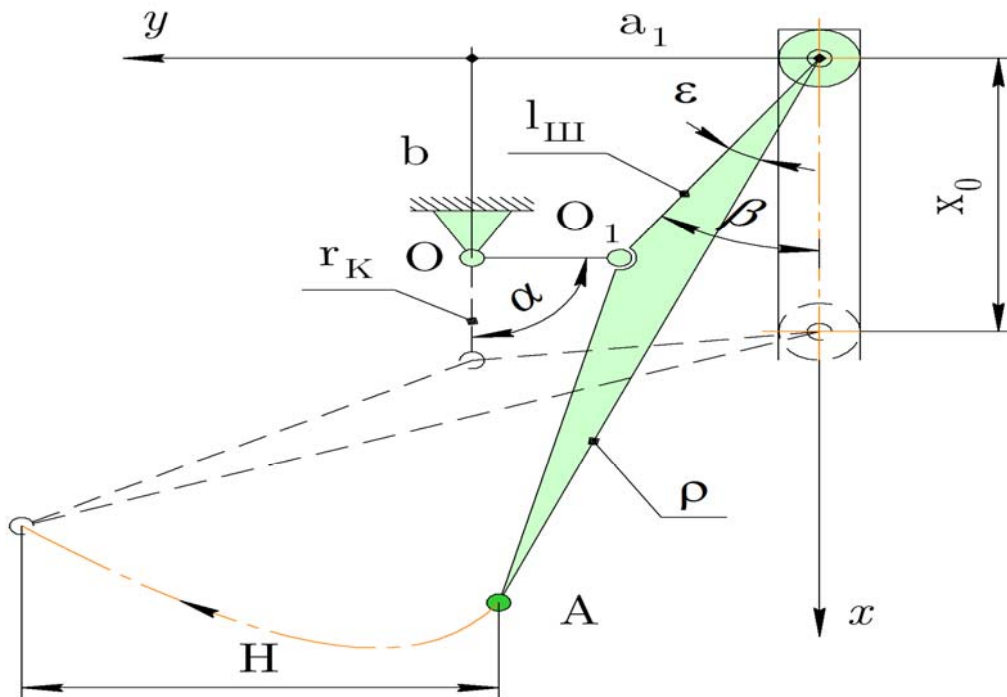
Кинематическая схема механизма раскрытия ковша со сложным движением козырька
